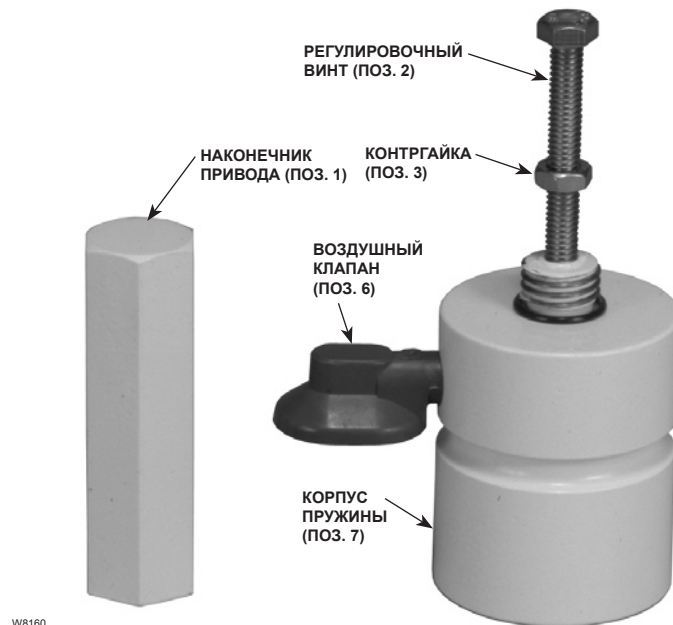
Корпус пружины, регулировочный винт и наконечник привода
